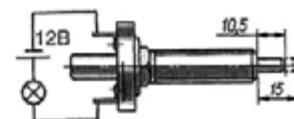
Проверка выключателя стоп-сигнала
